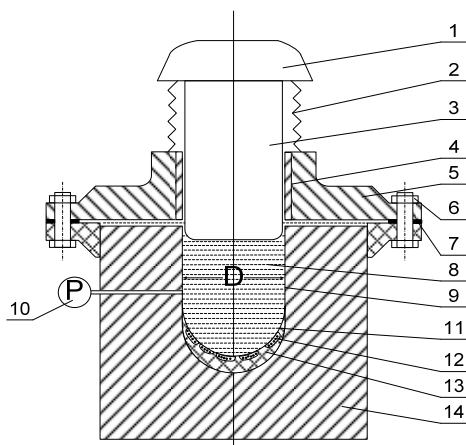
Устройство для обработки семян УД: 1 - оголовок; 2 - пружина; 3 - поршень; 4 - гильза; 5 - съемный цилиндр; 6 - болтовое соединение; 7 - прокладка; 8 - вода; 9 - цилиндрическая емкость; 10 - манометр; 11 - ткань; 12 - семена; 13 - контейнер; 14 - защитный кожух
